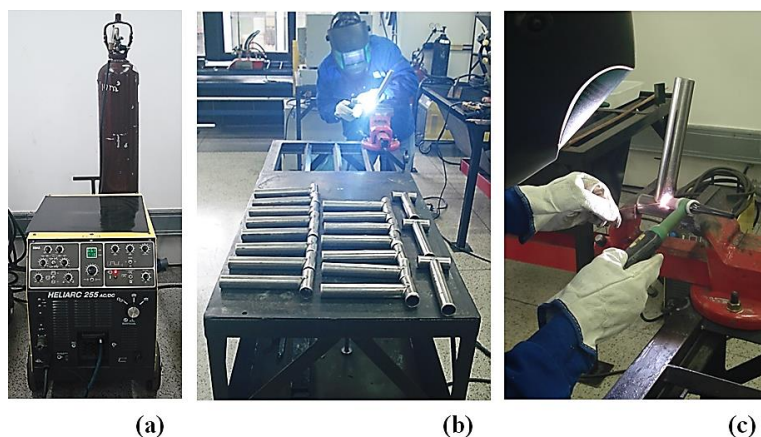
Processo de soldagem. (a) máquina de soldagem utilizada. (b) pontilhamento. (c) término com filete de solda.
